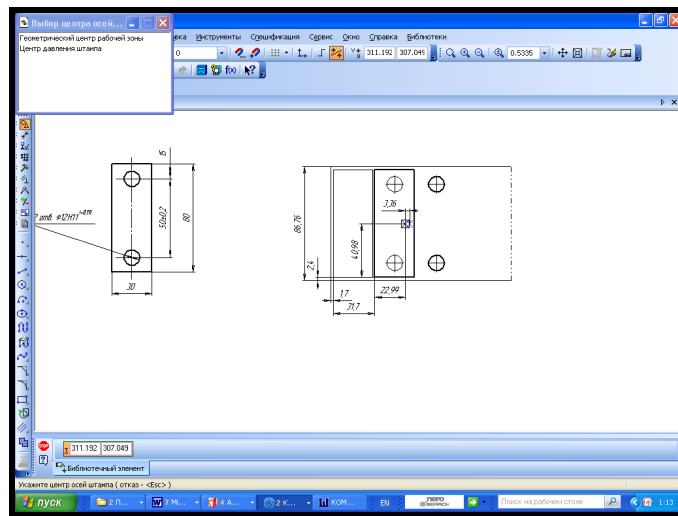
Геометричний центр робочої зони та центр тиску штампа
